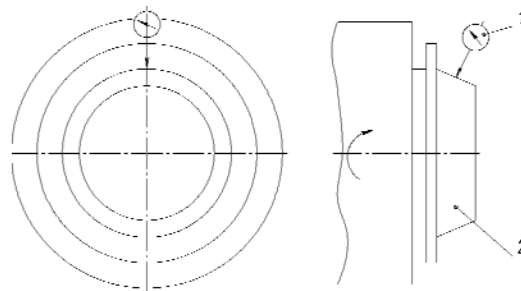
Схема перевірки геометричної точності конічної центрувальної поверхні шпинделя
